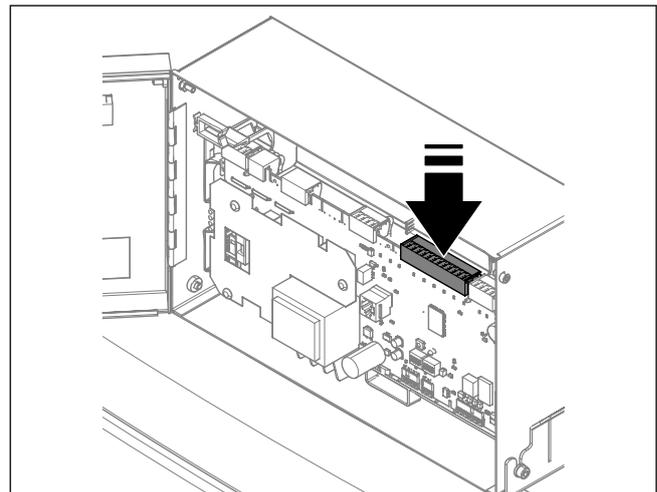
Sensorstecker J8 auf Schaltfeldplatine aufstecken
